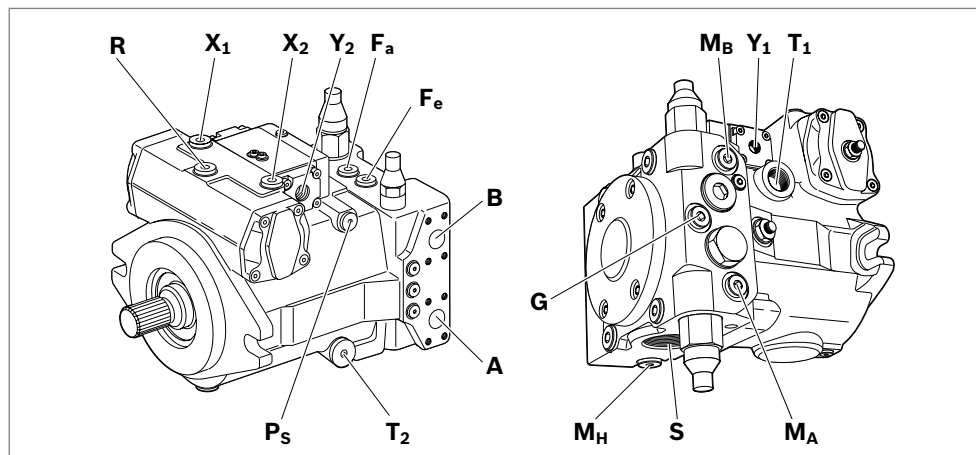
Vue d'ensemble des raccords A4VG, dimension nominale 28
